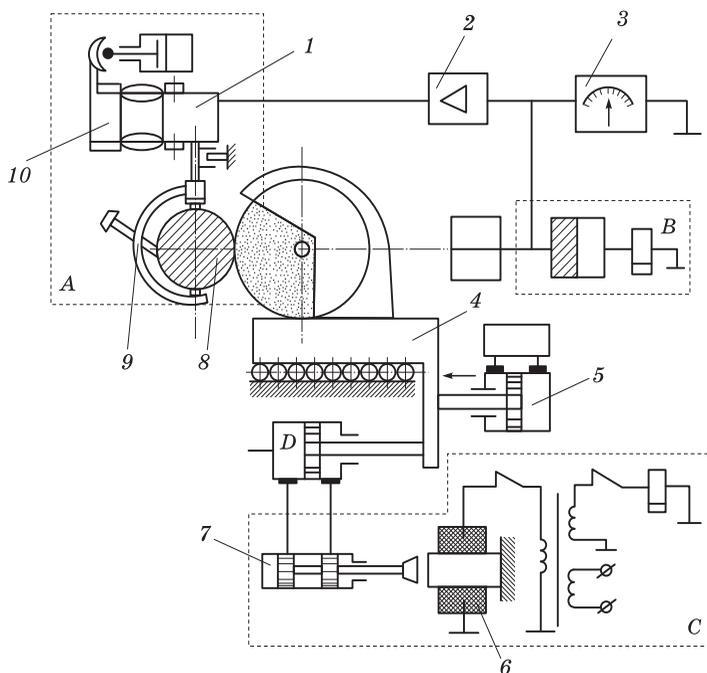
Схема устройства активного контроля круглошлифовального станка
